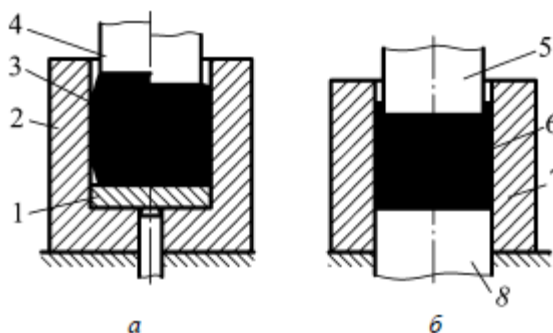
Схемы осадки в закрытом штампе: а – свободная осадка; б – осадка с образованием заусенца; 1, 8 – выталкиватели; 2, 7 – матрицы; 3, 6 – заготовки; 4, 5 – пуансоны
